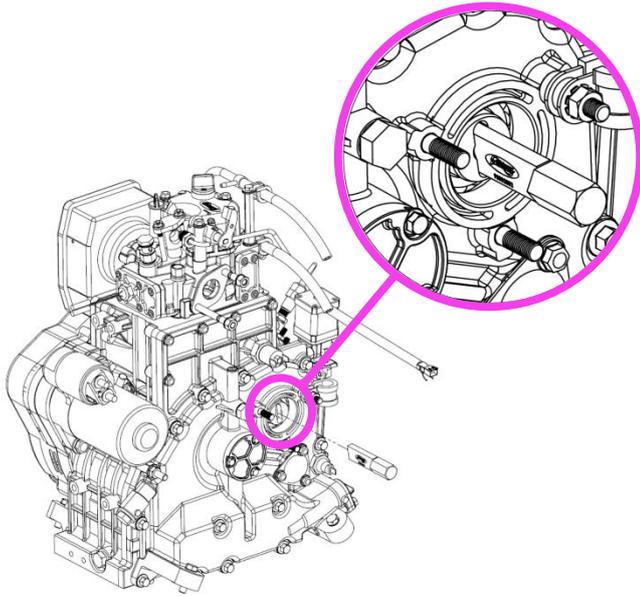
Drehwerkzeug zum Anfahren der oberen Totpunktposition
